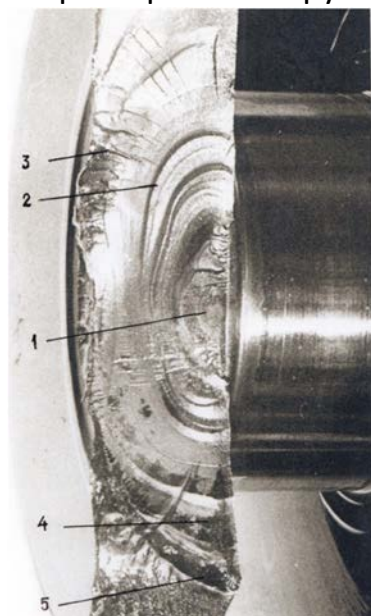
Схема усталостного излома щеки коленчатого вала:
